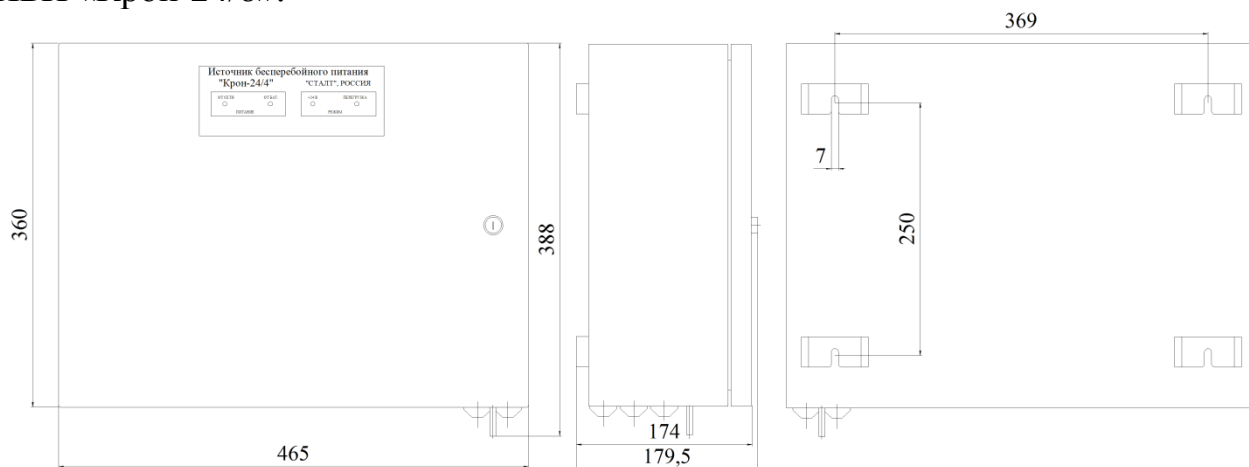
Габаритный чертёж ИБП «Крон-12/4», «Крон-12/8», «Крон-24/4» и «Крон-24/8» (типоразмер корпуса № 2)
